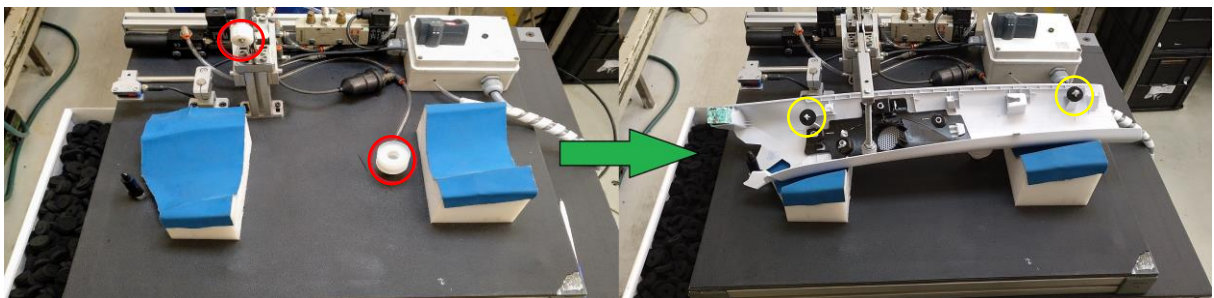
Método de fixação da bancada de montagem G do posto de injeção do molde 9288
